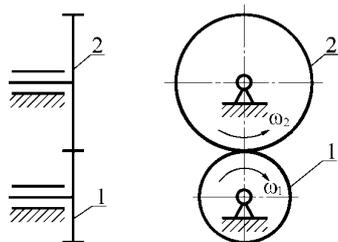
Зубчатая цилиндрическая передача внешнего зацепления
